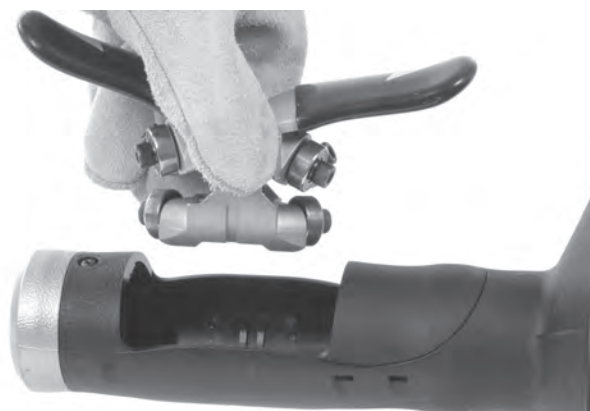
B – Снятие с корпуса устройства автоподачи AUTOFEED
